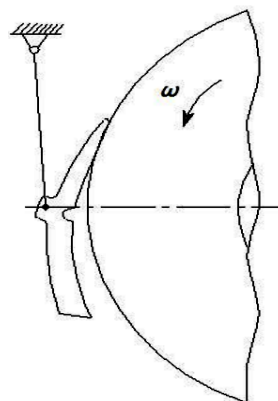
Загальний вигляд клиноподібного спрацювання колодки
